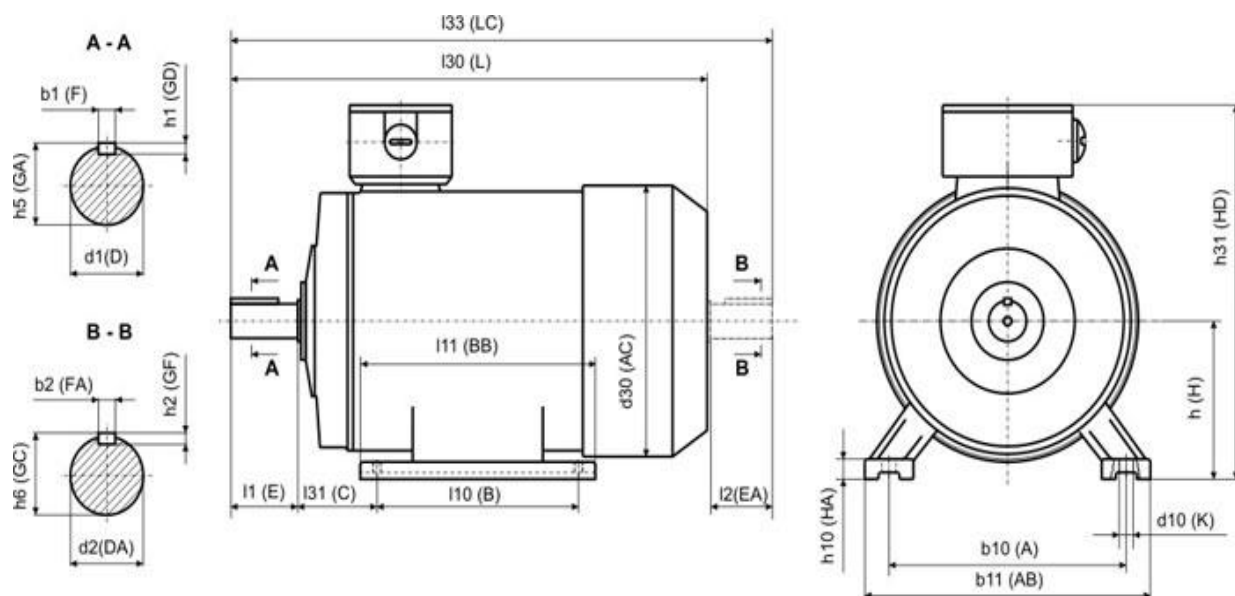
,17, Габаритные и присоединительные размеры двигателя
